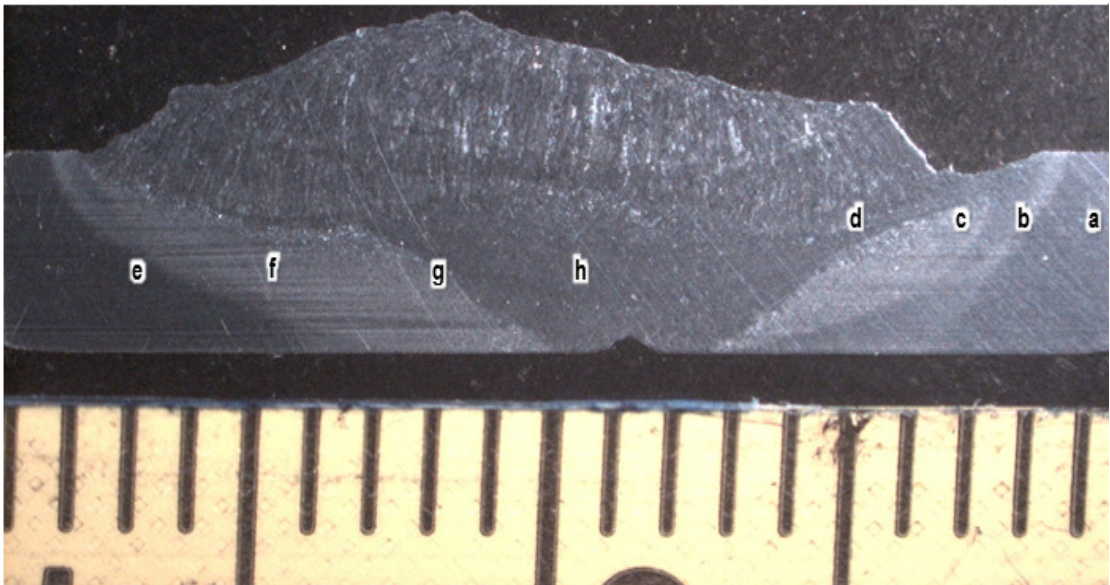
Macrografía de soldadura y metalografías de las diferentes zonas de la soldadura
